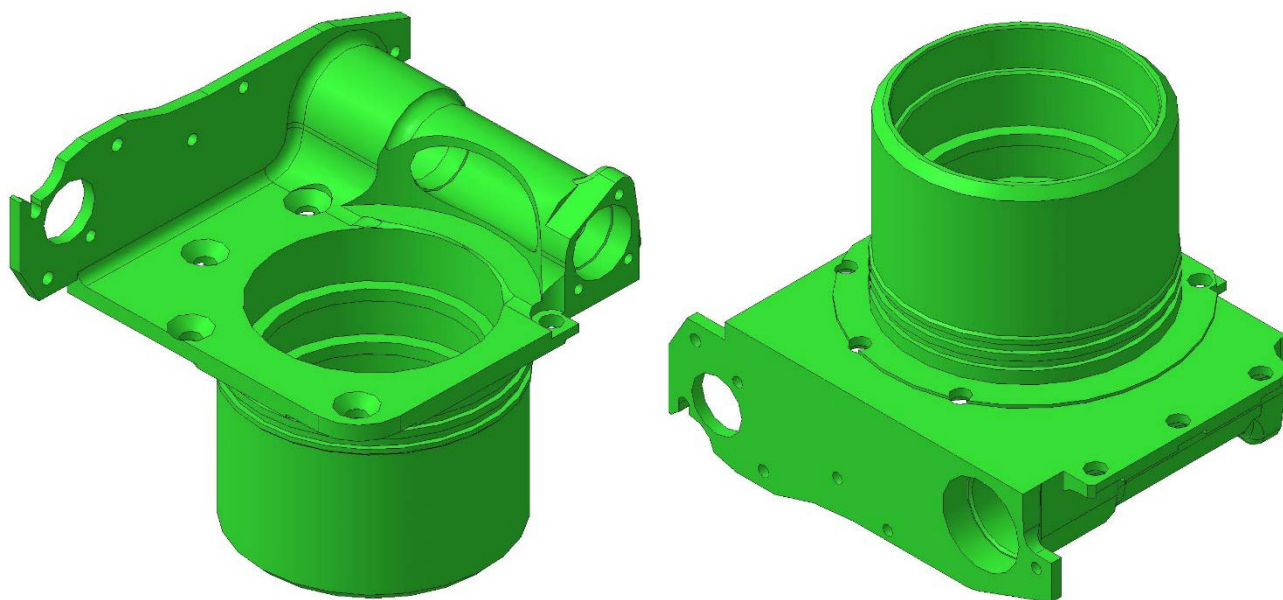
3D-модель детали «Корпус червячного редуктора»
